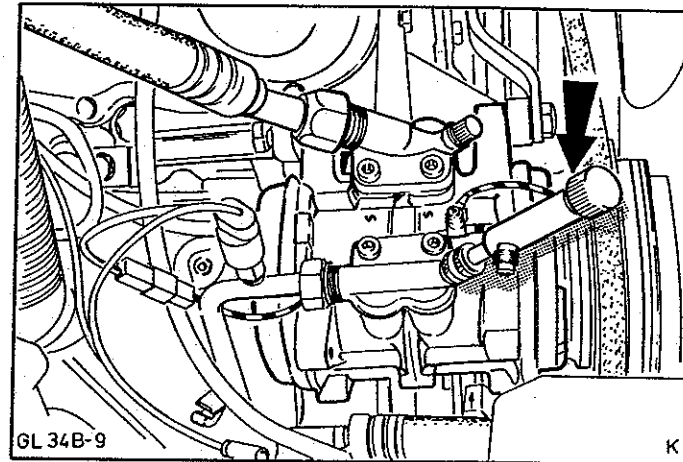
Kältemittel über Druckventil am Kompressor mit Ventilkernentferner ablassen
